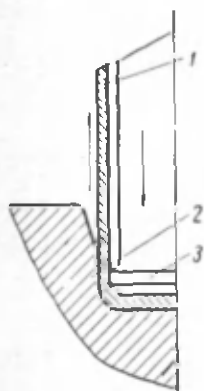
Вытяжка цинкового цилиндрического стакана фигурным пуансоном:
